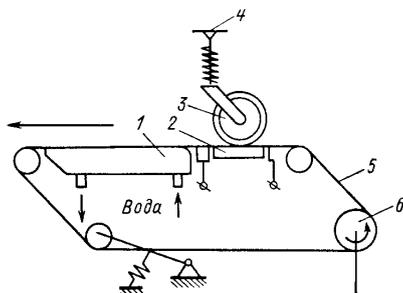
Схема термоконтактной сварки пленок:
